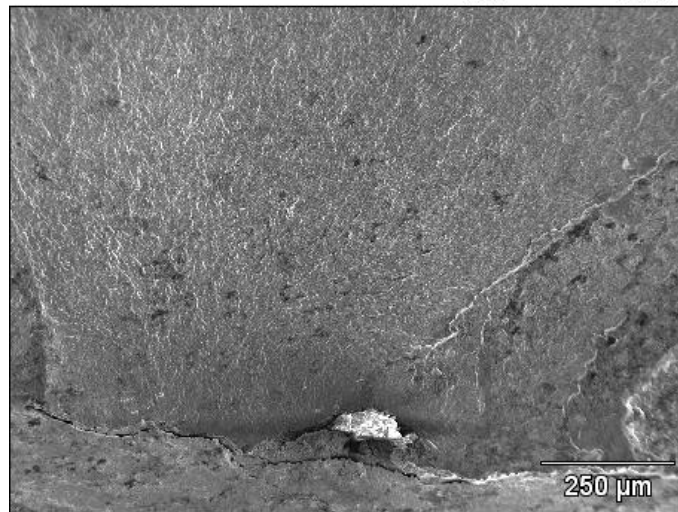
Detalle de la zona de iniciación de la grieta.
